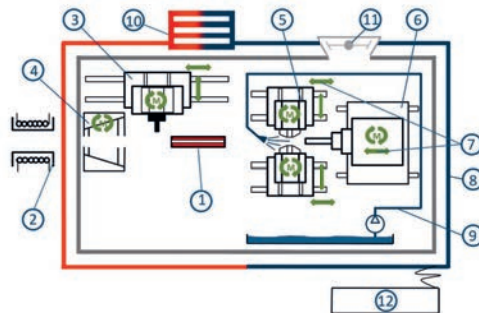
Maschinenkonzept der Bohrungsrückanlage (BDA)
